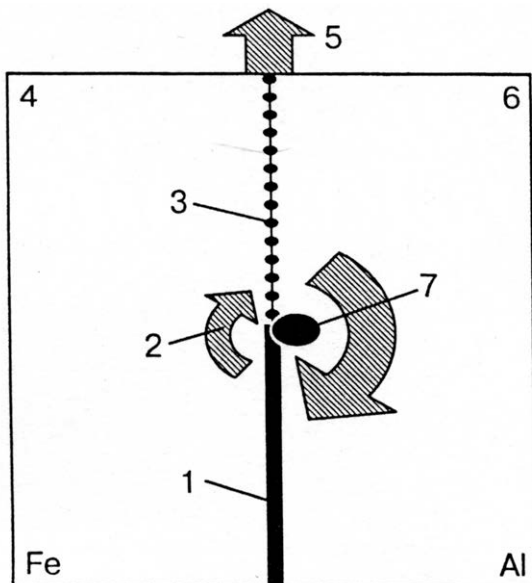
Технологическая схема СТП алюминиевого сплава со сталью: 1 – активируемая зона; 2 – направление вращения; 3 – неактивированная зона; 4, 6 – сторона сложения и разности векторов скоростей сварки и вращения инструмента; 5 – направление сварки; 7 – инструмент
